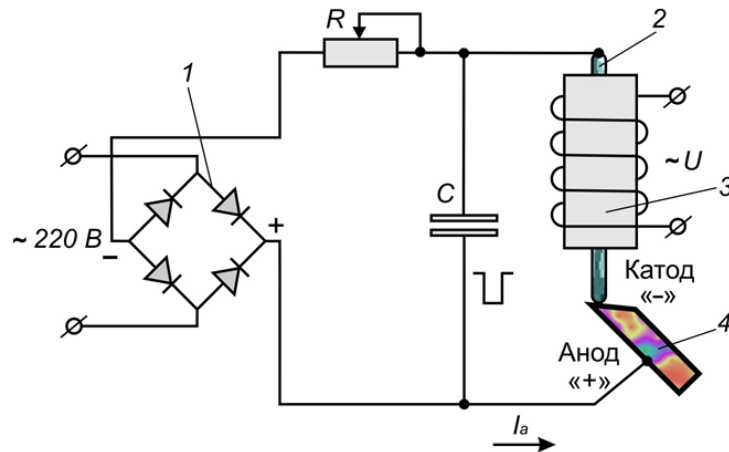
Принципова схема електроіскрового зміцнювання: 1 – діодний випрямляч напруги; 2 – інструмент-електрод; 3 – електромагнітний вібраційний пристрій; 4 – заготовка-ніж; R – регулювальний опір; C – конденсаторний генератор імпульсів; I_a – анодний струм
